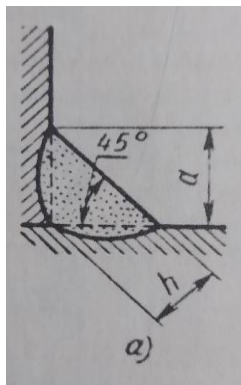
Sección transversal de la soldadura con costura normal. Fuente: Dobrovolski (1980).
